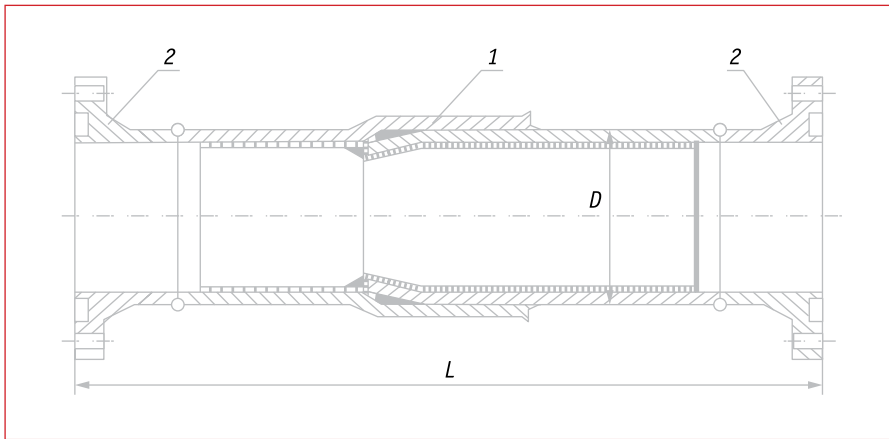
Схема образца в виде трубной катушки, представляющей собой раструбное соединение отрезков труб с фланцами на свободных концах:
